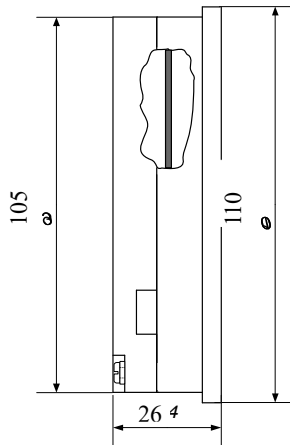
Габаритный чертеж ПЛК серии МС. Вид сбоку.
